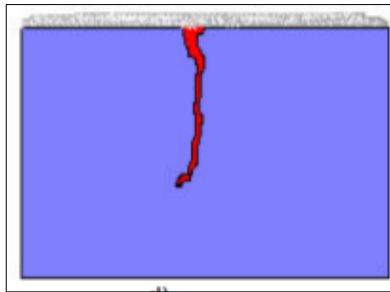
Rociado de revelador sobre la superficie de inspección.
